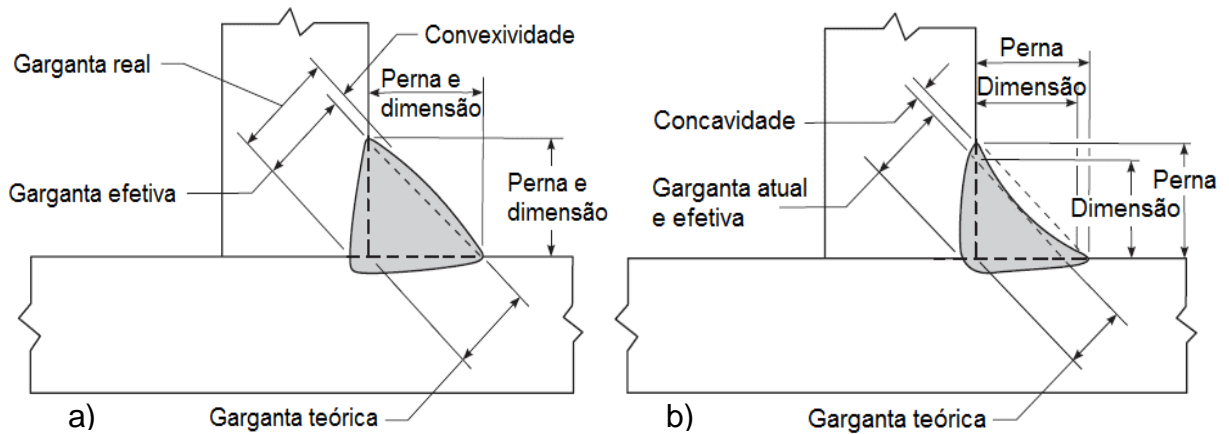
Dimensões da solda de filete em junta "T": a) solda convexa; b) solda côncava.
